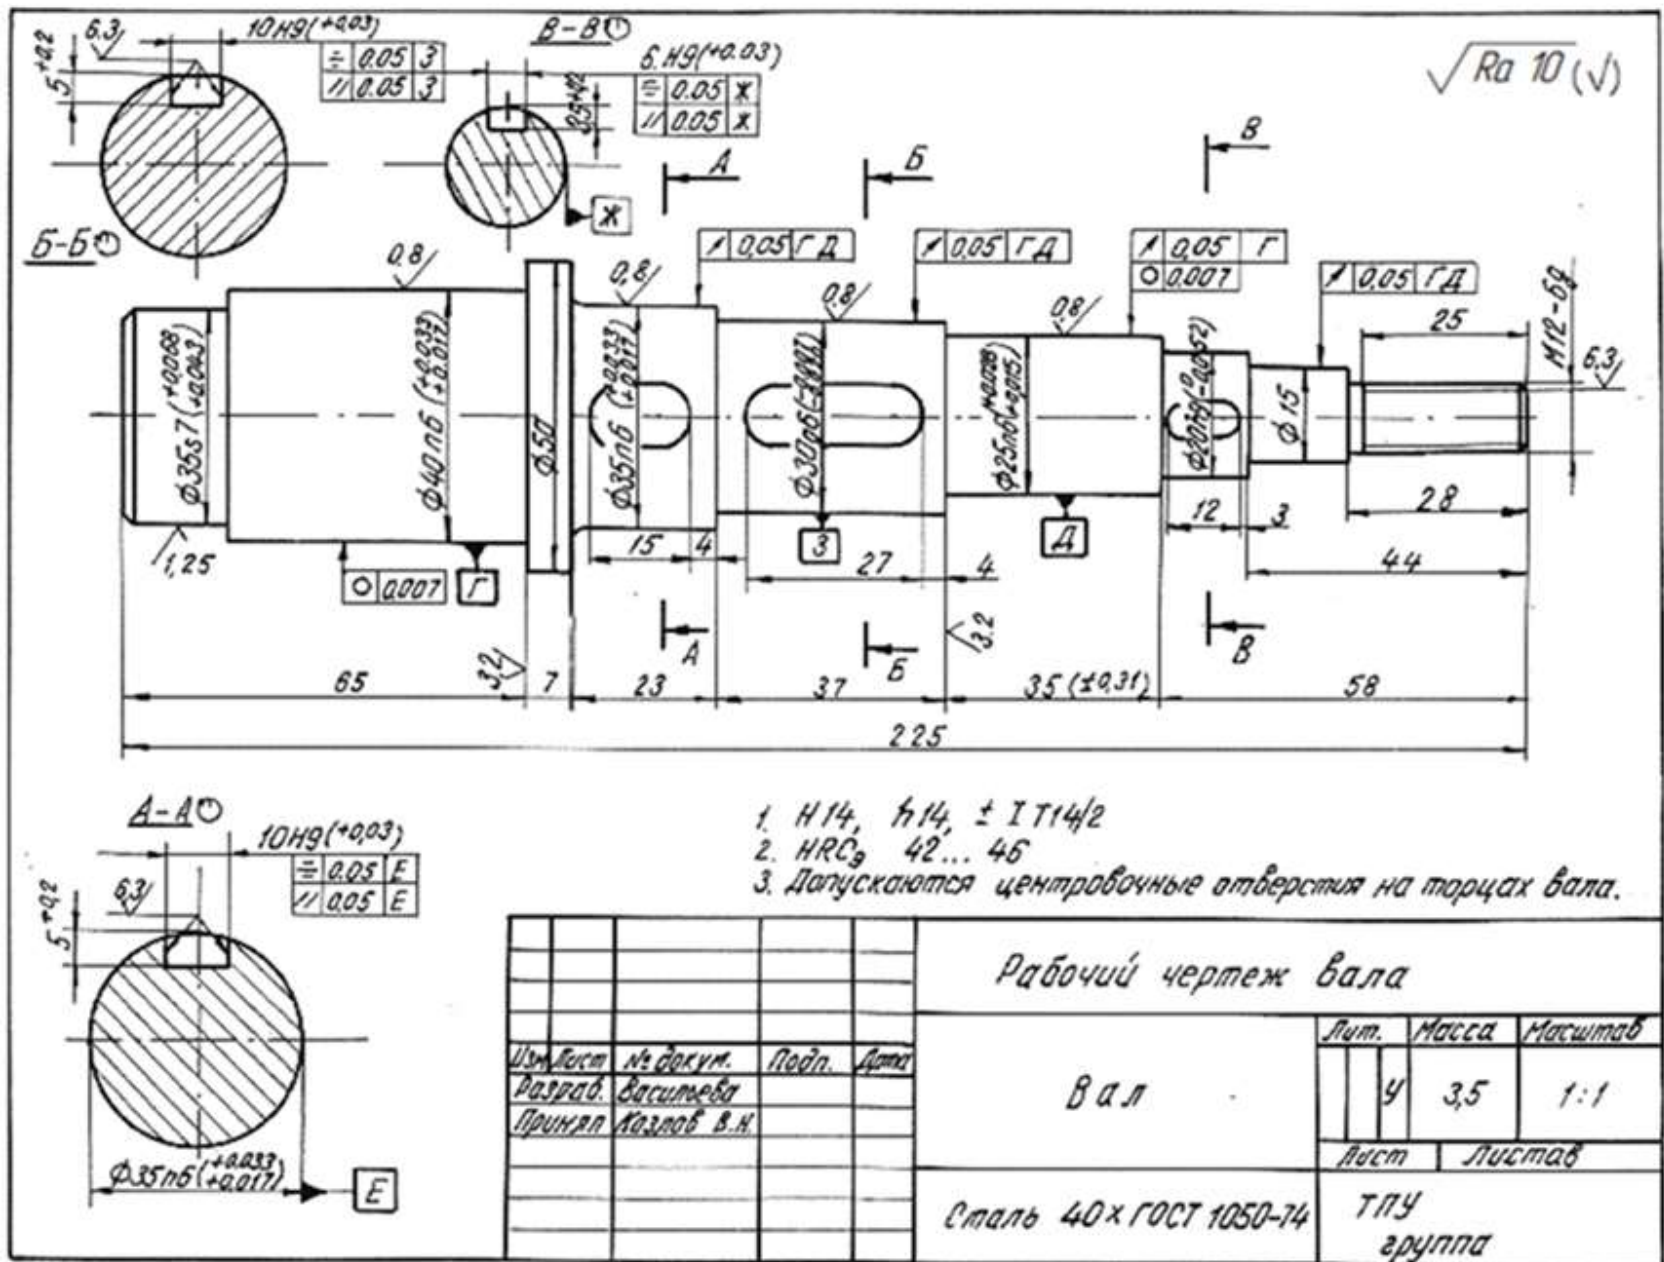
Пример чертежа (эскиза) детали «Вал» из сборочного чертежа рис. 4.62.
